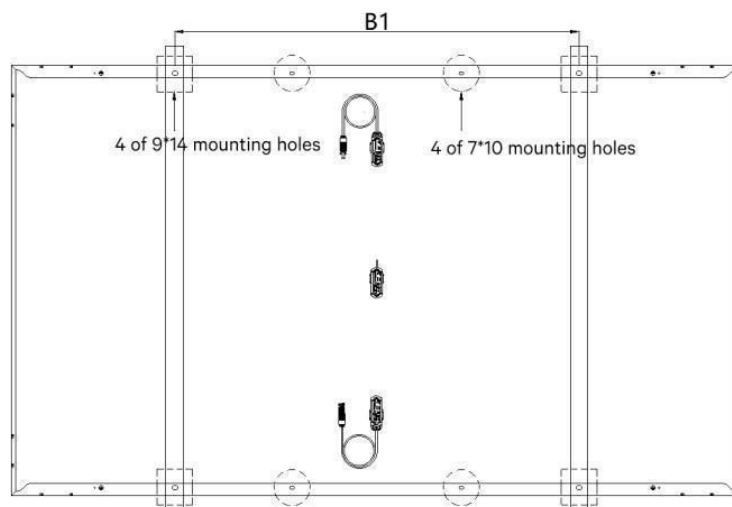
Método de fixação com parafusos (4 orifícios de montagem)
